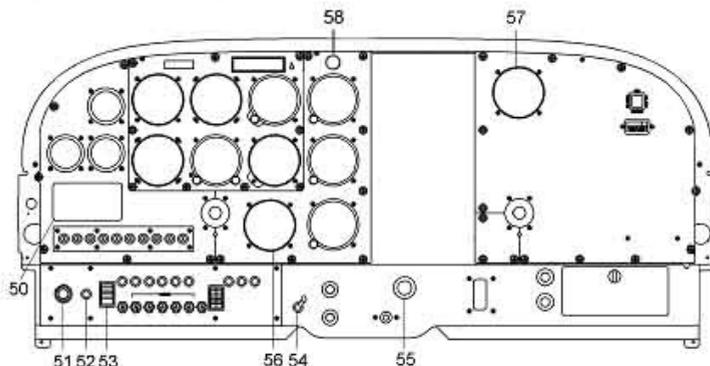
Beispiel Instrumentenbrett mit TAE 125 Installation
